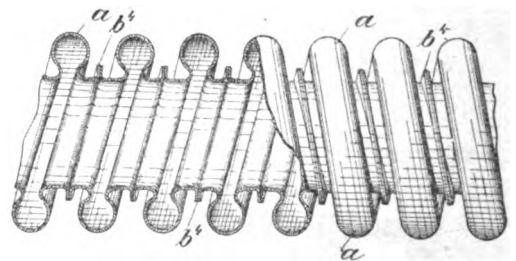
34. Geschweißter Schlauch, schraubenförmig gewickelt.
